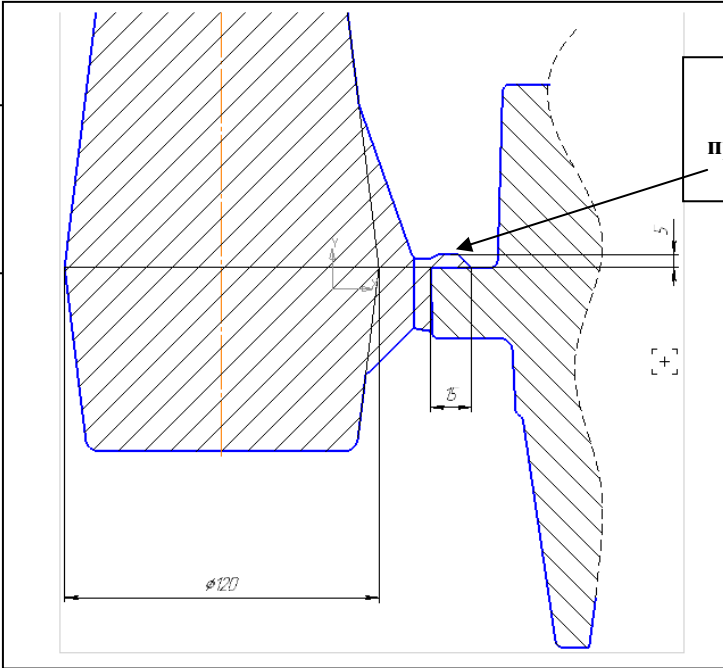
Чертеж отливки 101.02.70.208 Корпус
